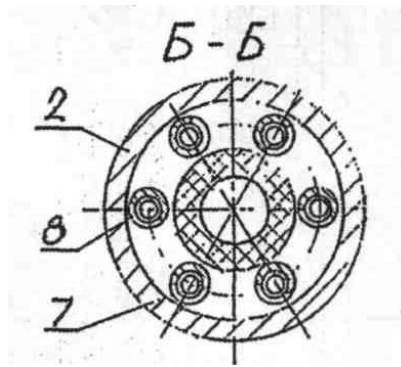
Переріз снаряду через корпус з гнучкими елементами
